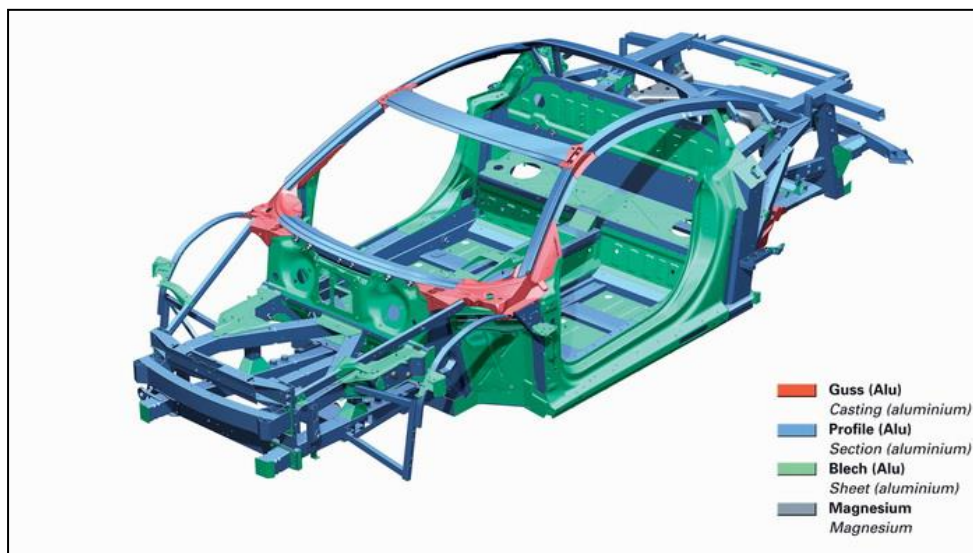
Xassís amb parts de magnesi (Font: <http://www.tecmovia.com>)
